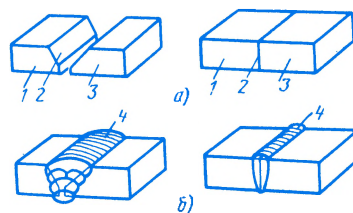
Соединение деталей сваркой плавлением:
